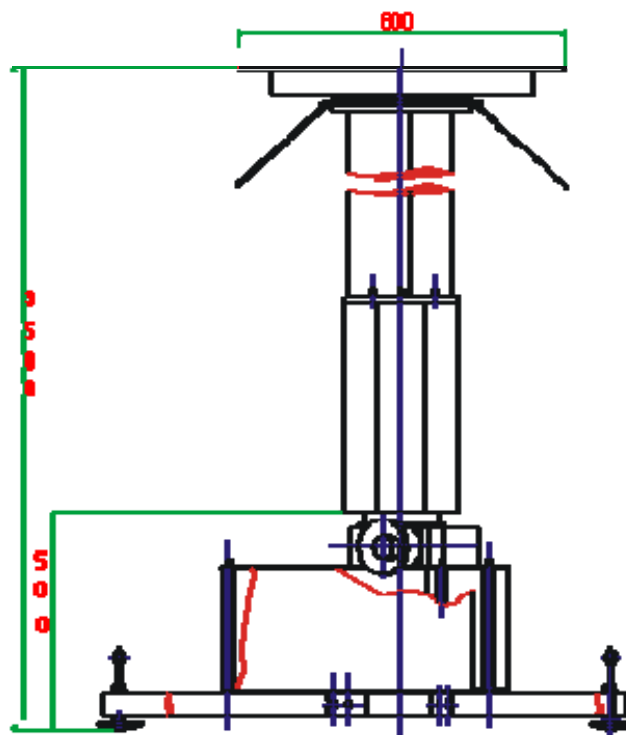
Габаритный чертеж ОПУ с мачтой.
